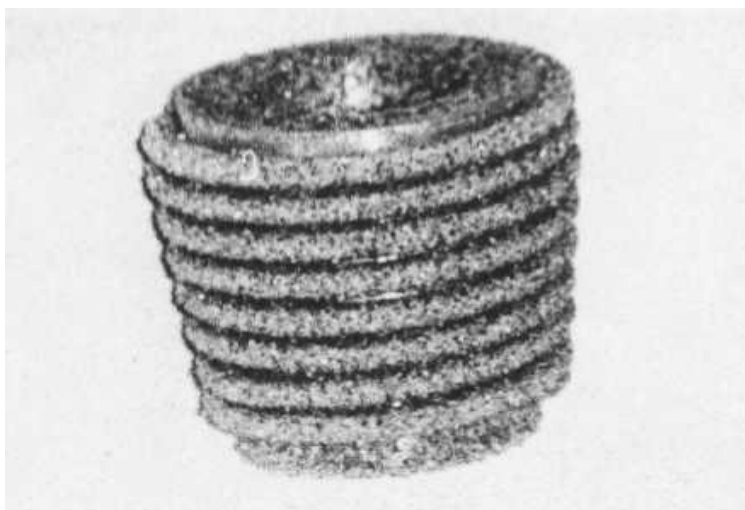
Макетный образец рабочего органа картофелечистки непрерывного действия
